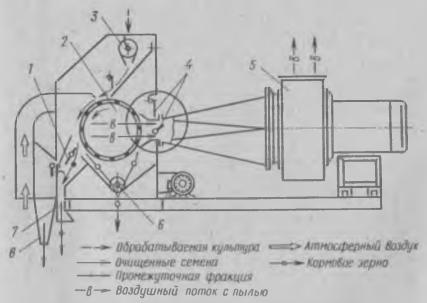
Центробежно-пневматический сепаратор ЗАВ-40.02.000: I— заслонка; 2— сетчатый барабан; 3— питающее устройство; 4— стабилизатор; δ — шеек; 7, 8— патрубки
